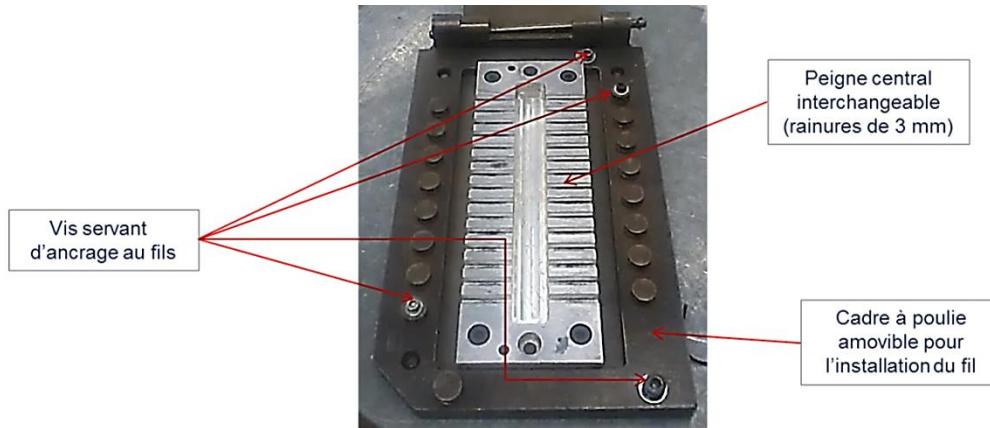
Moule pour élaboration d'éprouvettes de pull-out (destiné pour des applications caoutchouc à la base)
